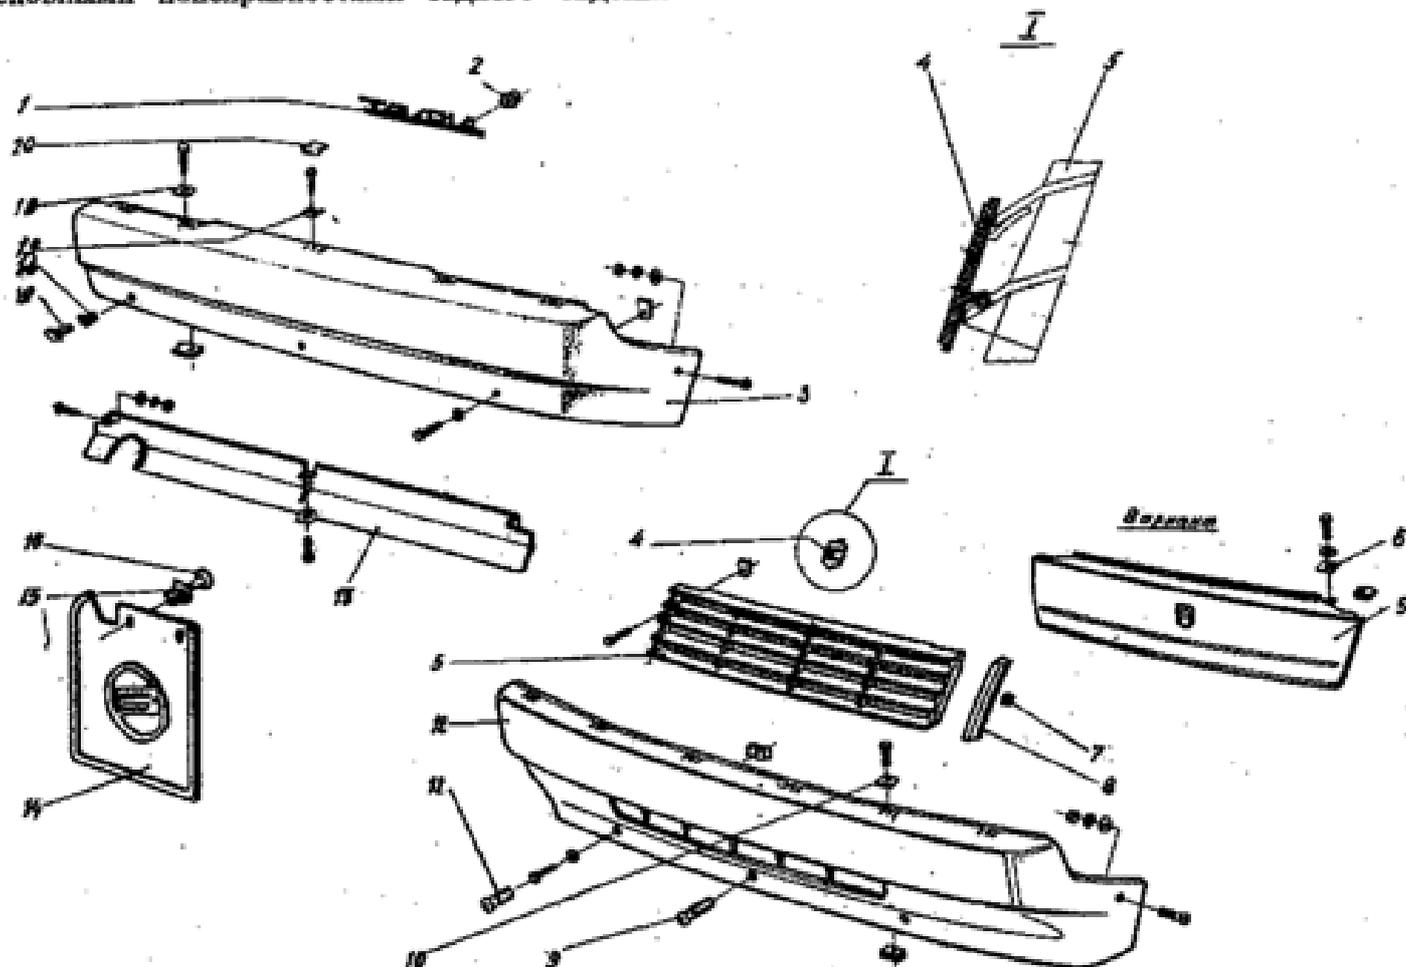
Бамперы, облицовка радиатора и декоративные надписи: 1 - надпись декоративная; 2 - втулка; 3 - бампер передний; 4 - знак заводской; 5 - облицовка радиатора; 6 - гайка специальная; 7 - держатель наставки; 8 - наставка облицовки радиатора; 9 - заглушка; 10 - пластина; 11 - заглушка; 12 - бампер передний; 13 - спойлер; 14 - фартук; 15 - втулка; 16 - пистон; 17 - заглушка; 18 - втулка заглушки; 19 - держатель; 20 - накладка декоративная.
